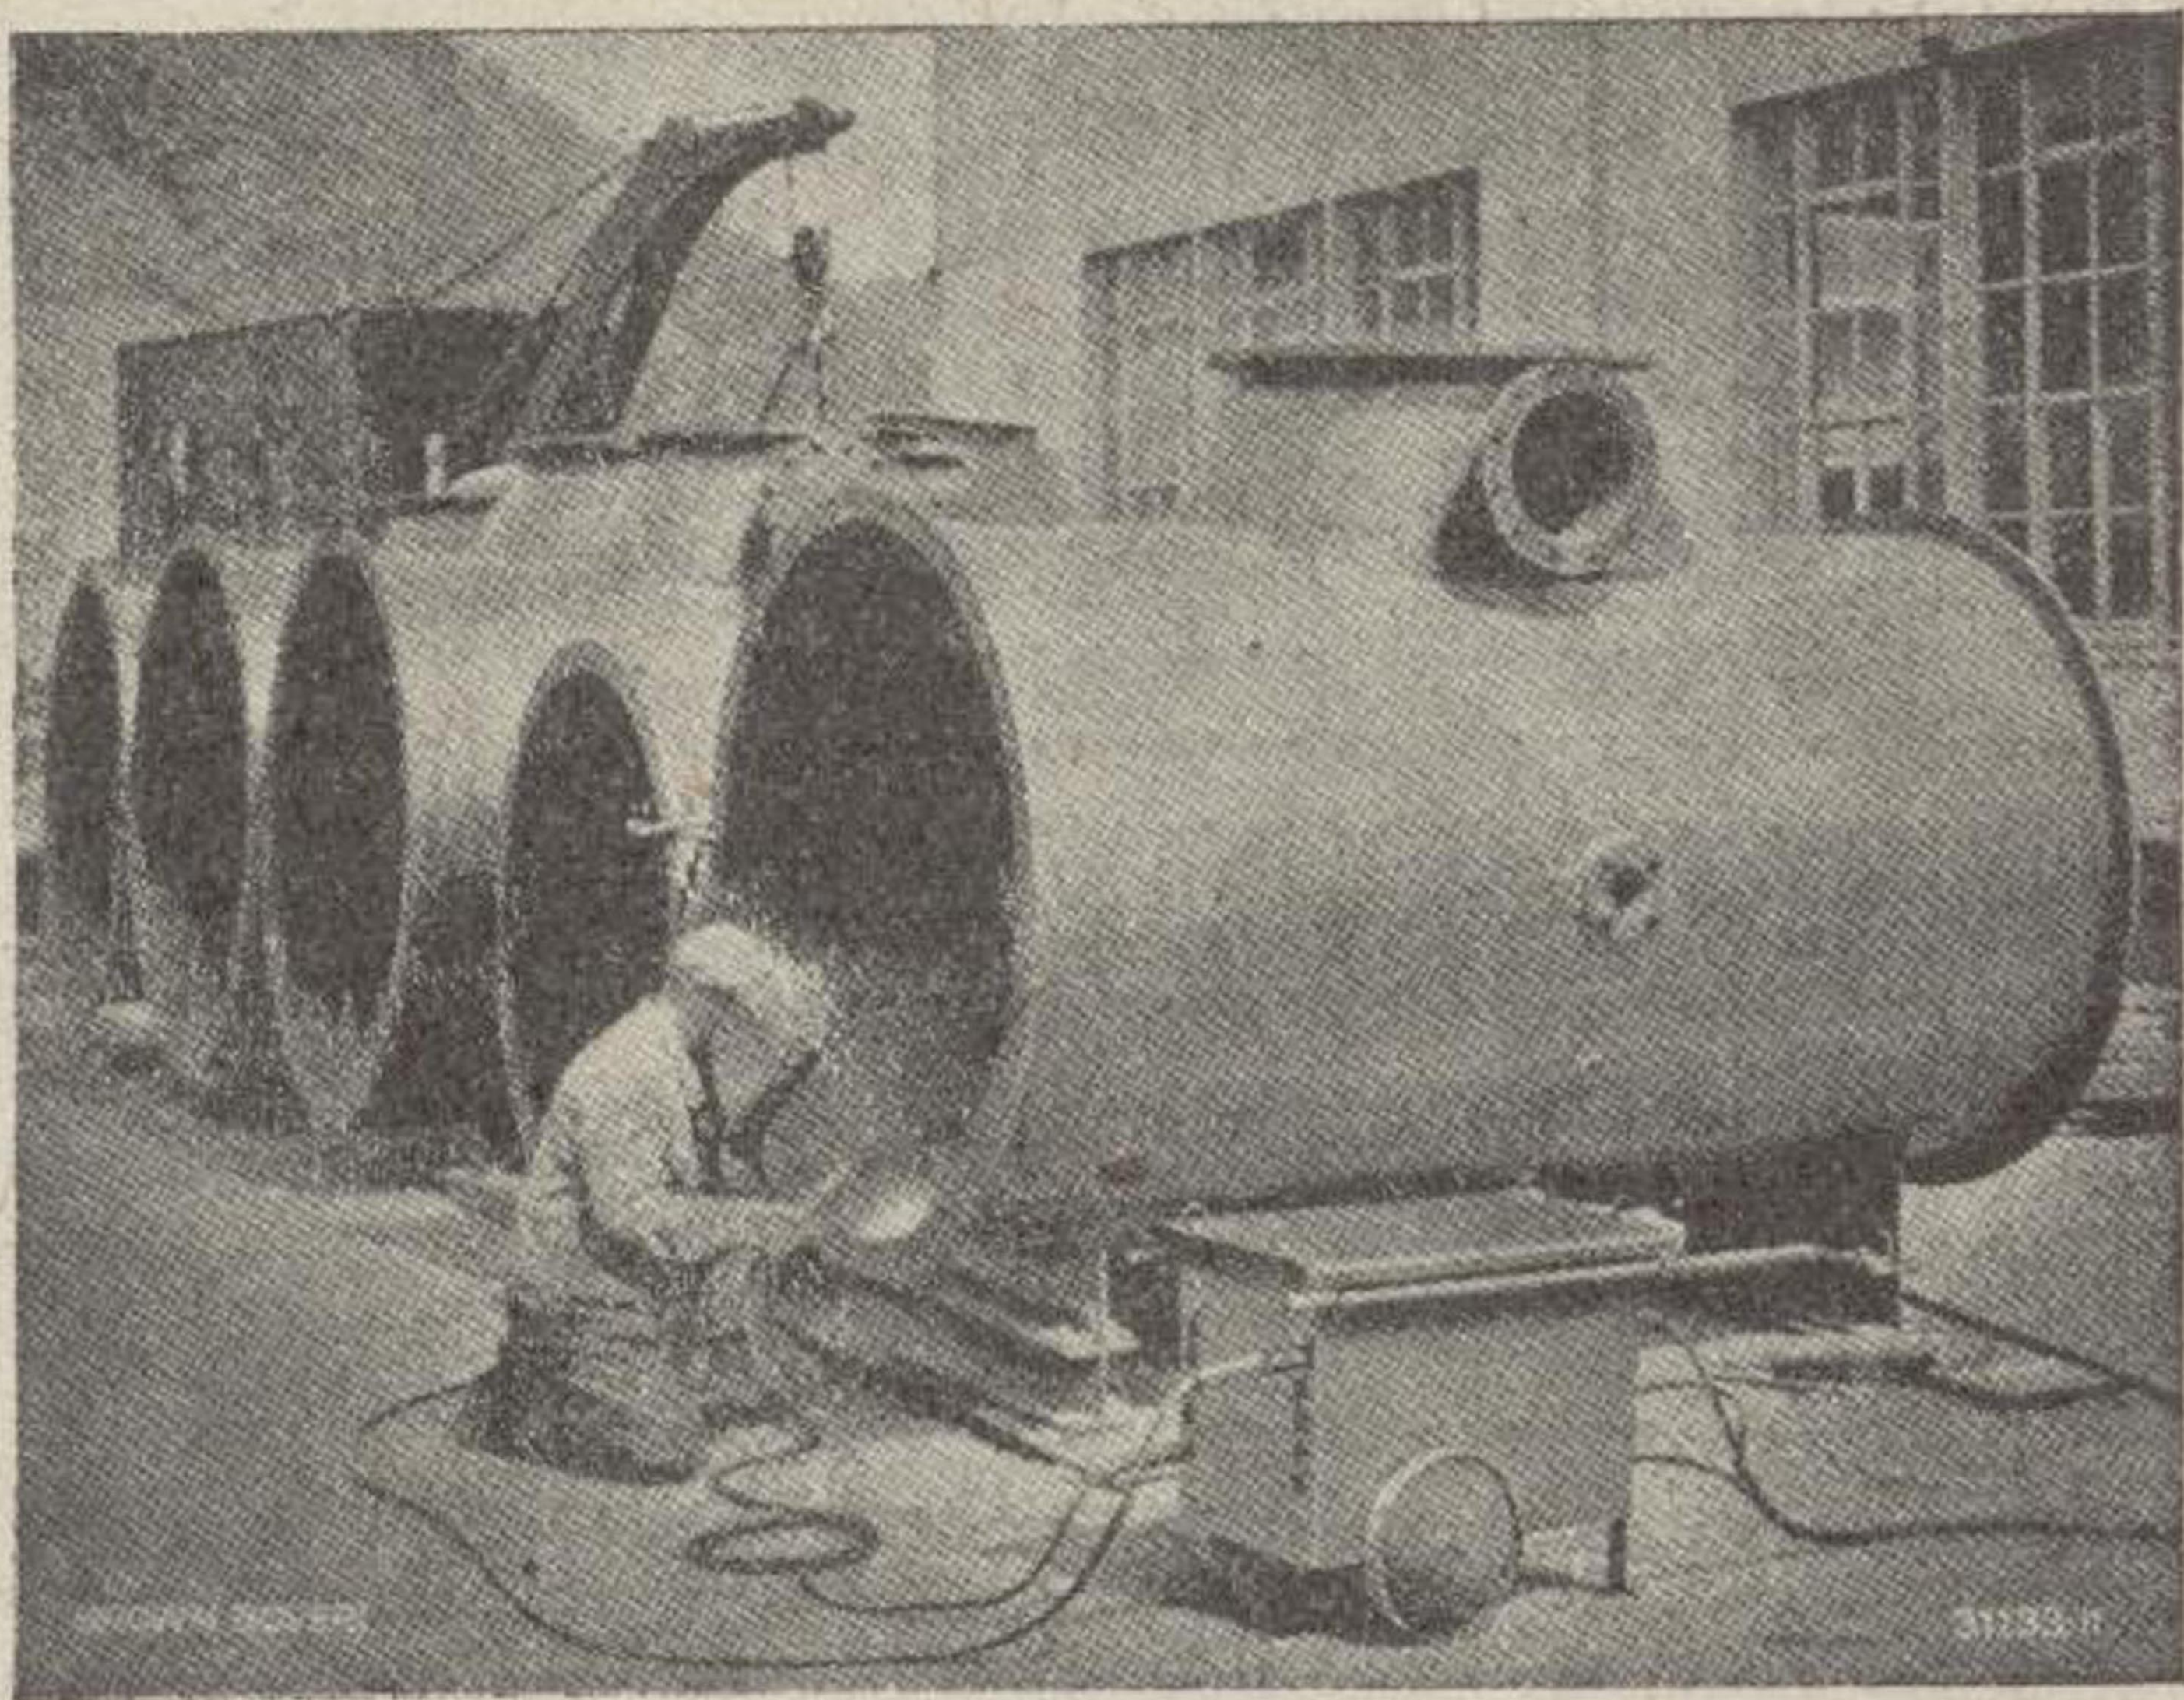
Un transformador durante la soldadura de envolvertes de condensadores.
